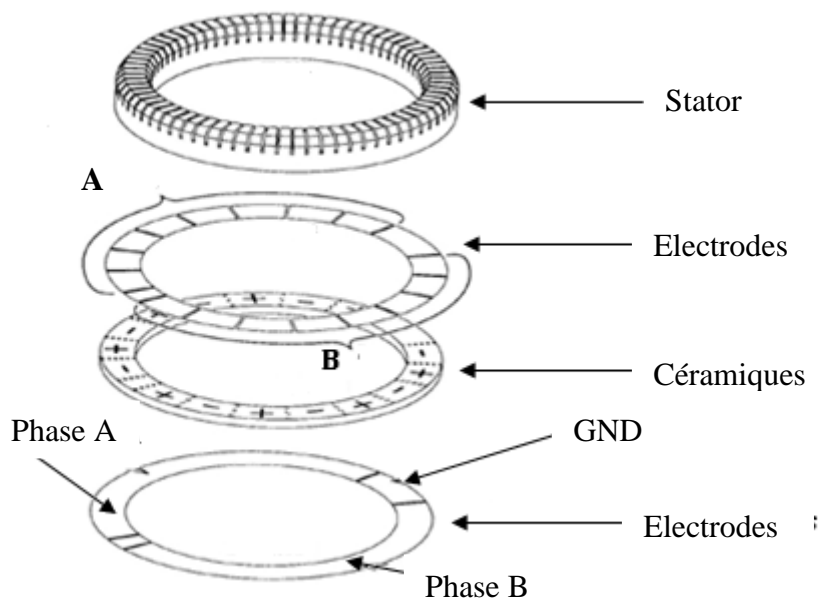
Le stator en forme éclatée du moteur SHINSEI USR60 [6].
